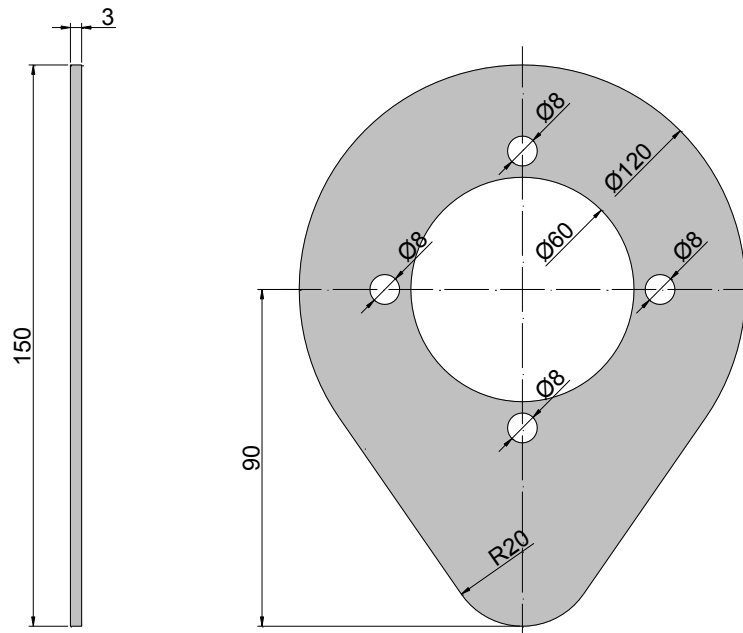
Suporte de anilha para a Autoclave, em perfil e planta, respetivamente
